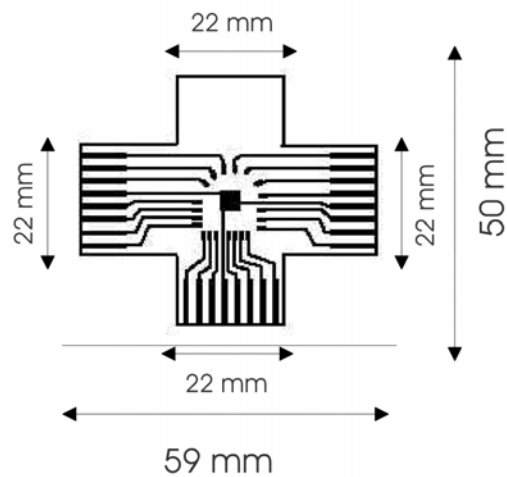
Esquema y dimensiones de la placa PCB de una sola cara diseñada para encapsulado de estructuras resonantes.
